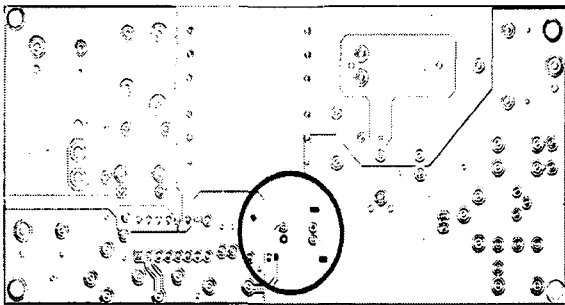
전처리 과정을 거친 검사 PCB 영상
